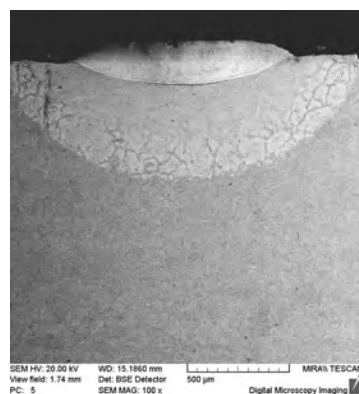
Поперечный шлиф валика, полученного лазерной наплавкой сплава ПГ-12Н-01 при скорости наплавки $V=60$ мм/мин и дистанции наплавки $L=12$ мм
